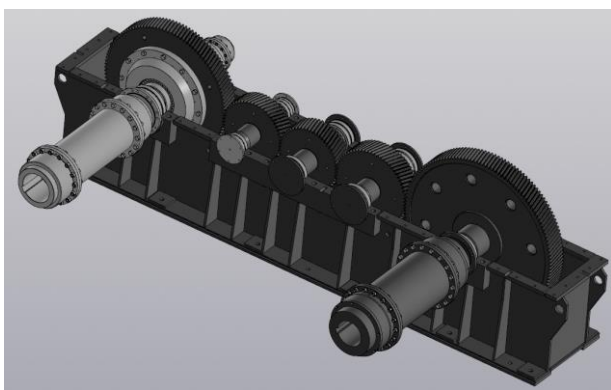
Главный редуктор изгибо-растяжной машины стана холодной прокатки
